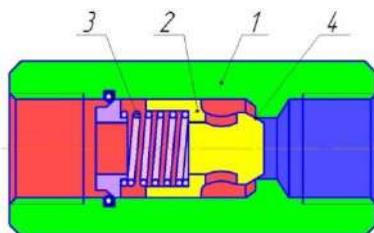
Зворотний клапан різьбового монтажу:
